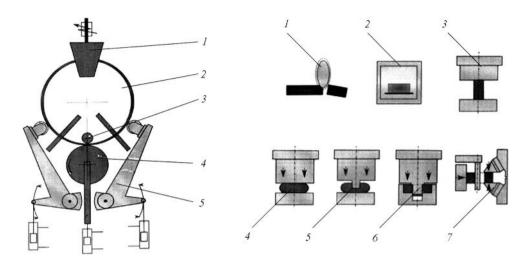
Рабочая схема радиально-осевой раскатки: *I* – осевые валки; *2* – кольцо; *3* – дорновой валок; *4* – главный валок; *5* – центрирующее устройство
